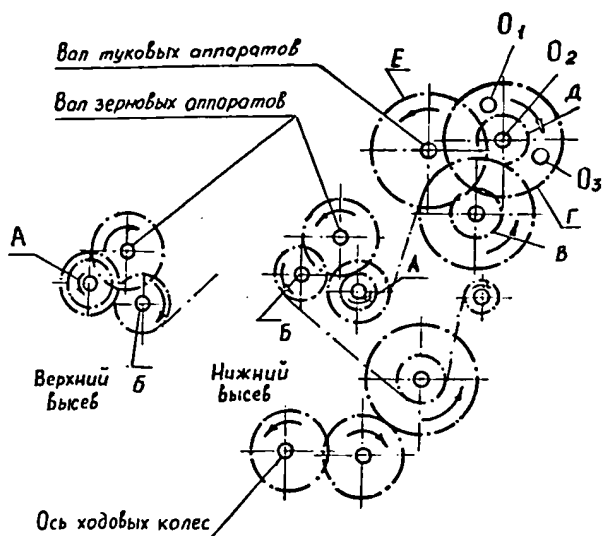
Схема настройки сеялки СУК-24А на верхний высеб
